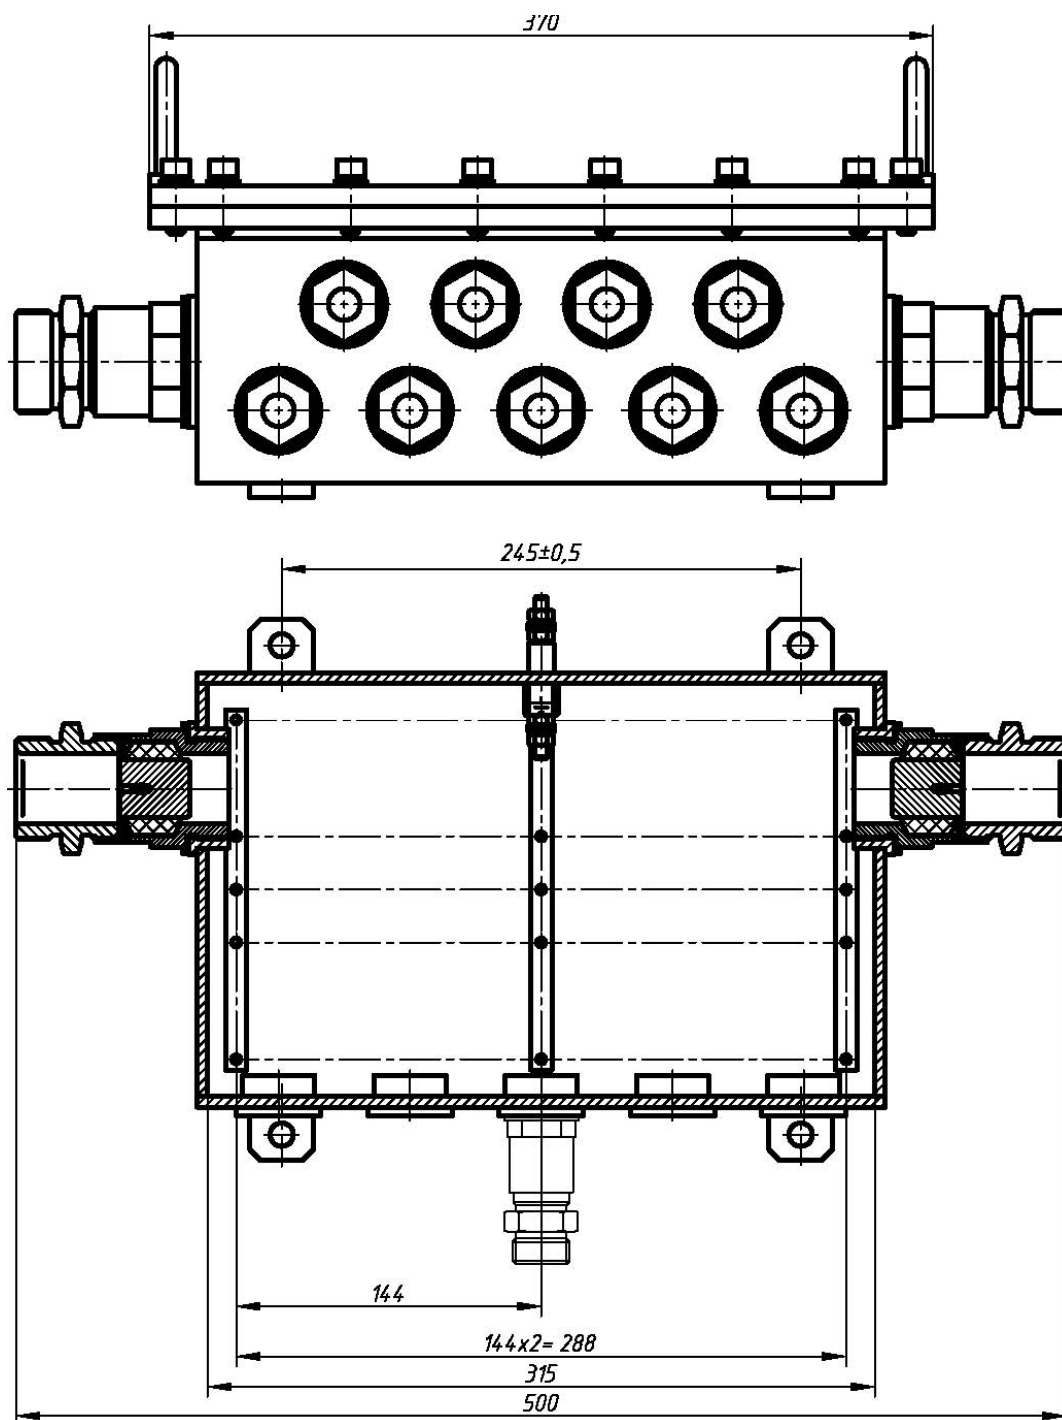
Габаритный чертеж коробки ЕхКСУВ-ПС370.
